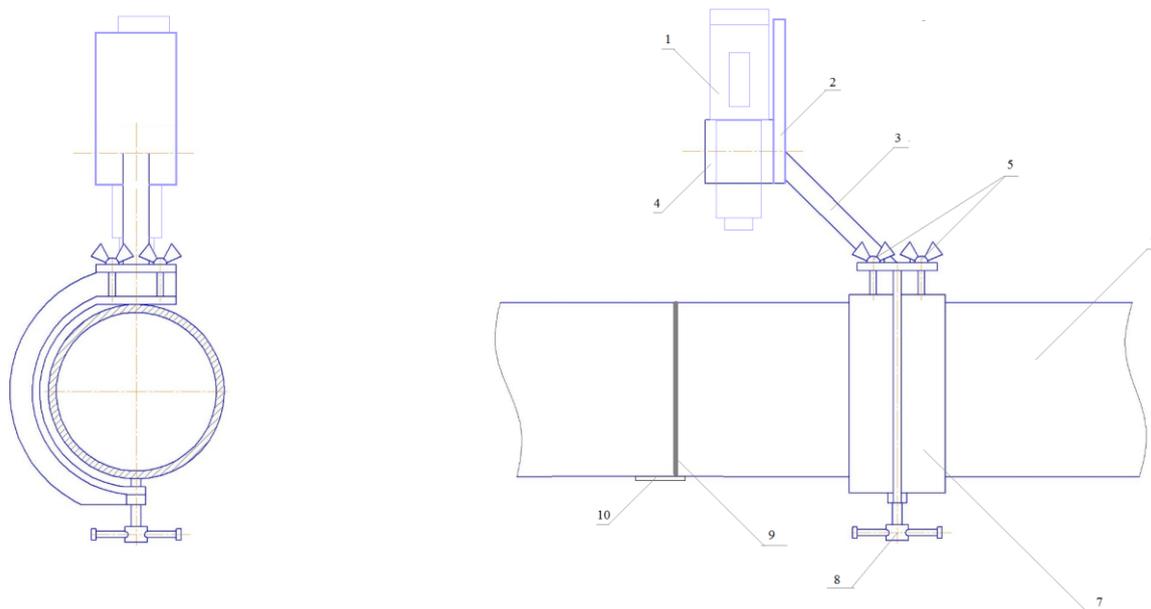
Конструкция приспособления для аппарата Арина-7: 1 – Арина – 7; 2 – направляющая опора; 3 – штанга; 4 – крепление; 5 – регулировочный винт; 6 – труба; 7 – скоба; 8 – запорный винт; 9 – сварочный шов; 10 – рентгенографическая пленка.
